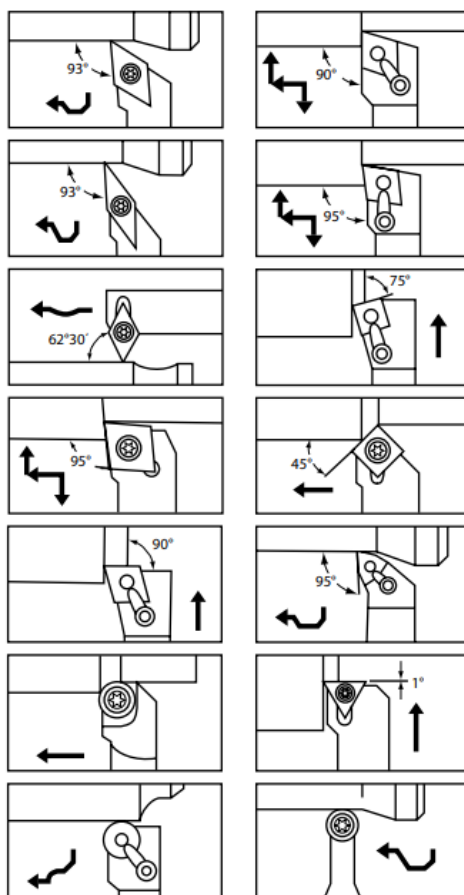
Обработка деталей с использованием сменных твердосплавных пластин
